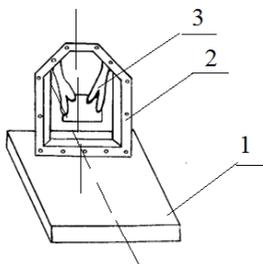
Схема сварки в камере с контролируемой атмосферой:
